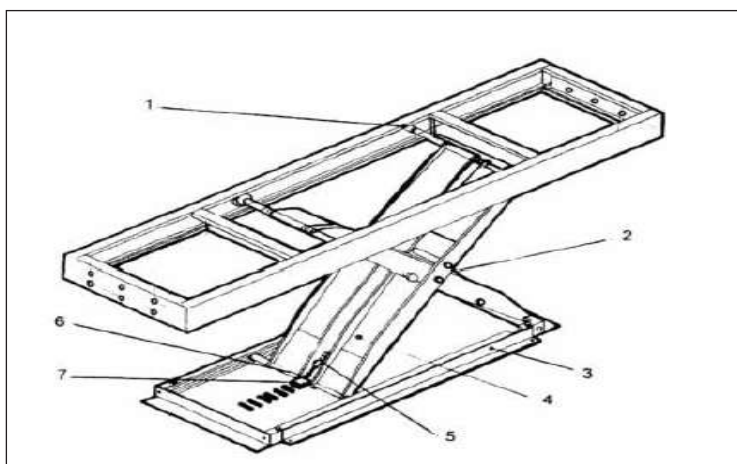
VISTA EN PERSPECTIVA DEL ELEVADOR
